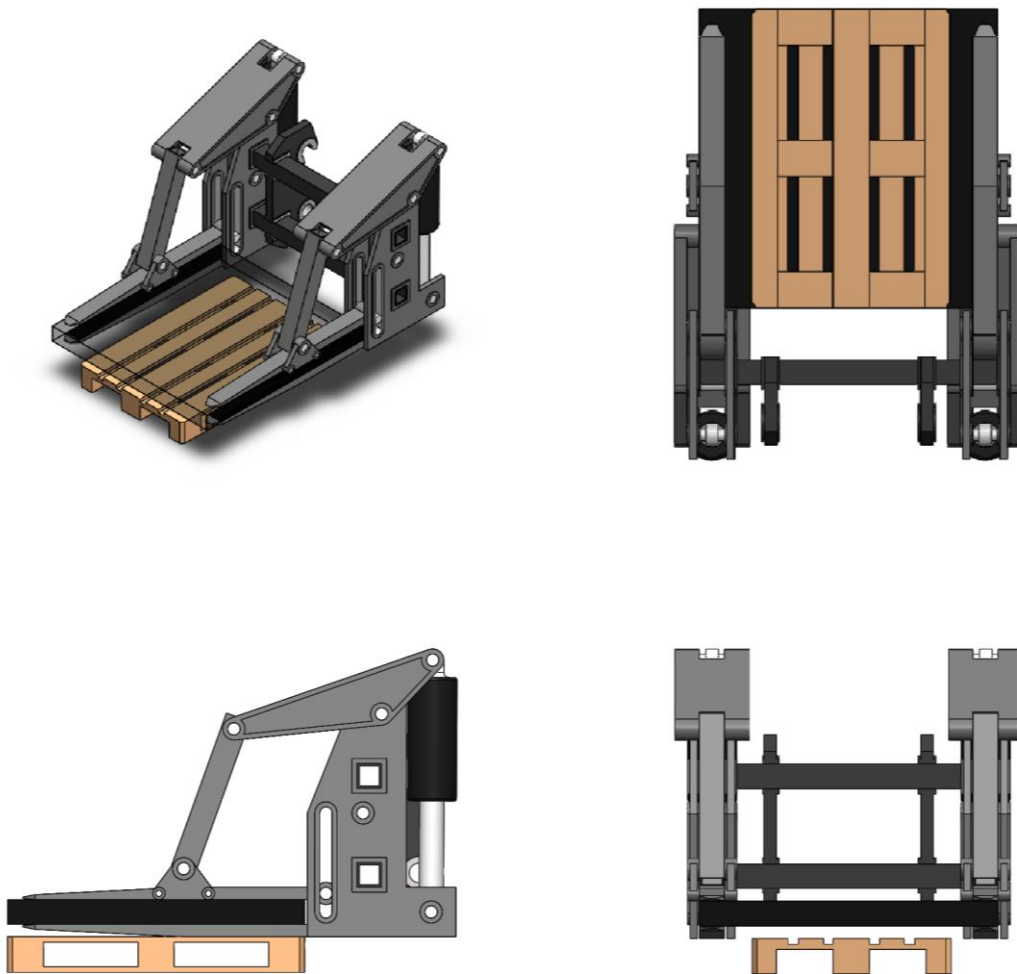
Col·locació de la capa de paviment arrencada sobre un palet.
